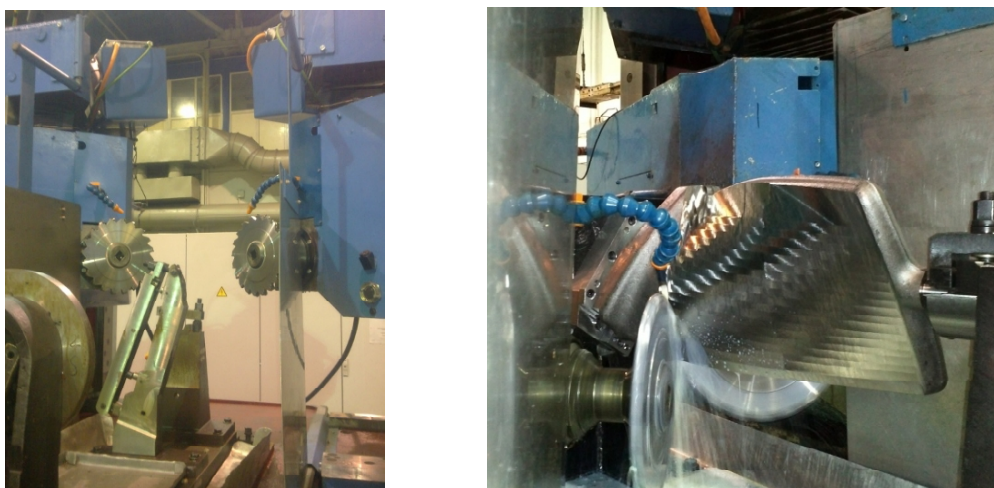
Фрезерование пера лопатки на станке 4ФСЛ-8П
